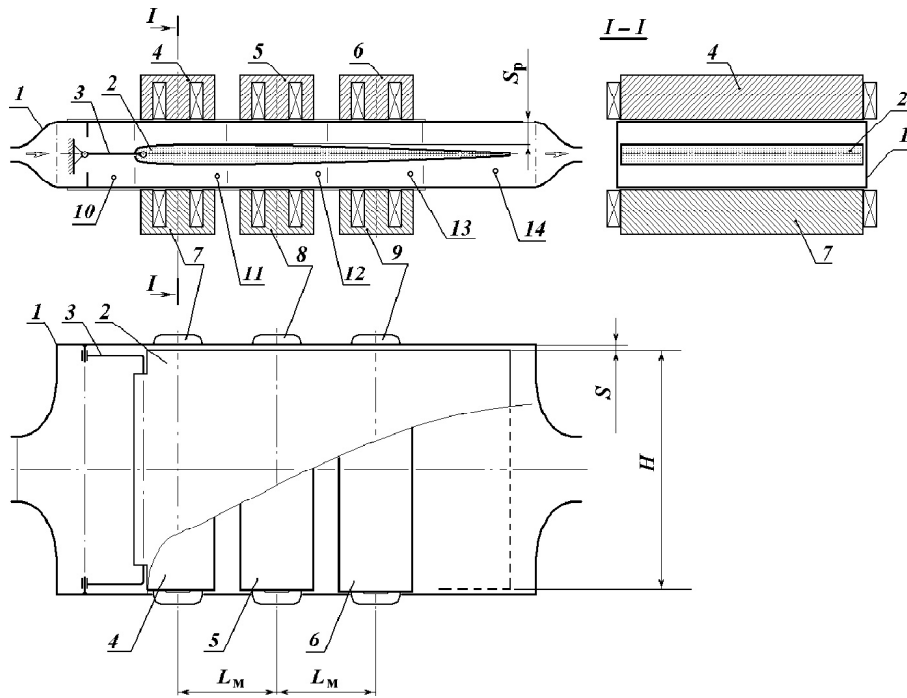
Конструктивна схема циркуляційного насоса:
